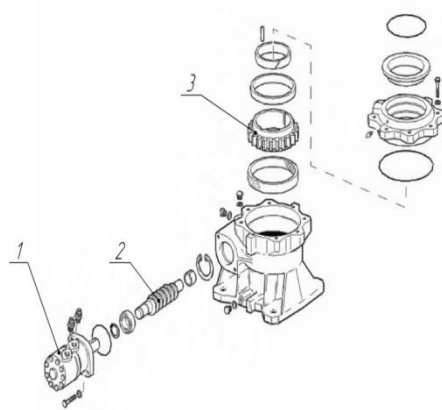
Опорно-поворотний пристрій на основі гідромотора та черв'ячної передачі
